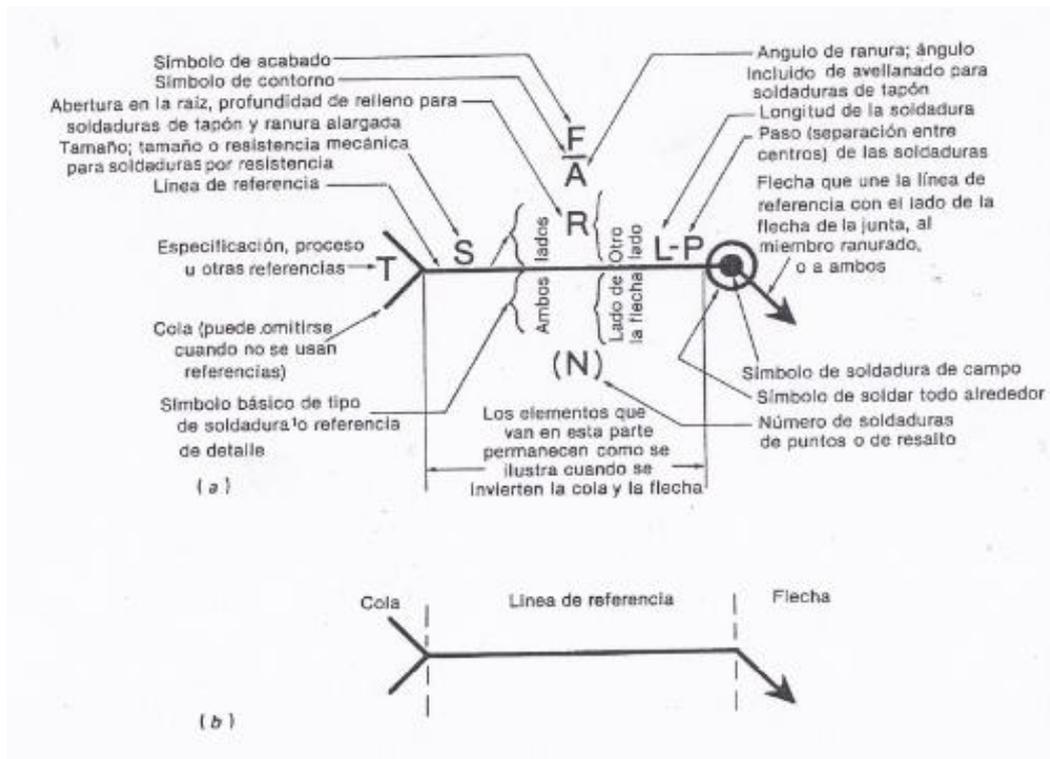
Elementos del Símbolo de Soldadura
